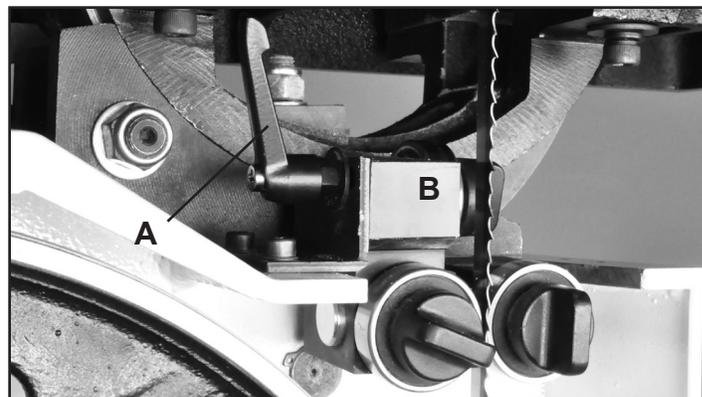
REMARQUE : Garde-lame retiré à des fins de photo
